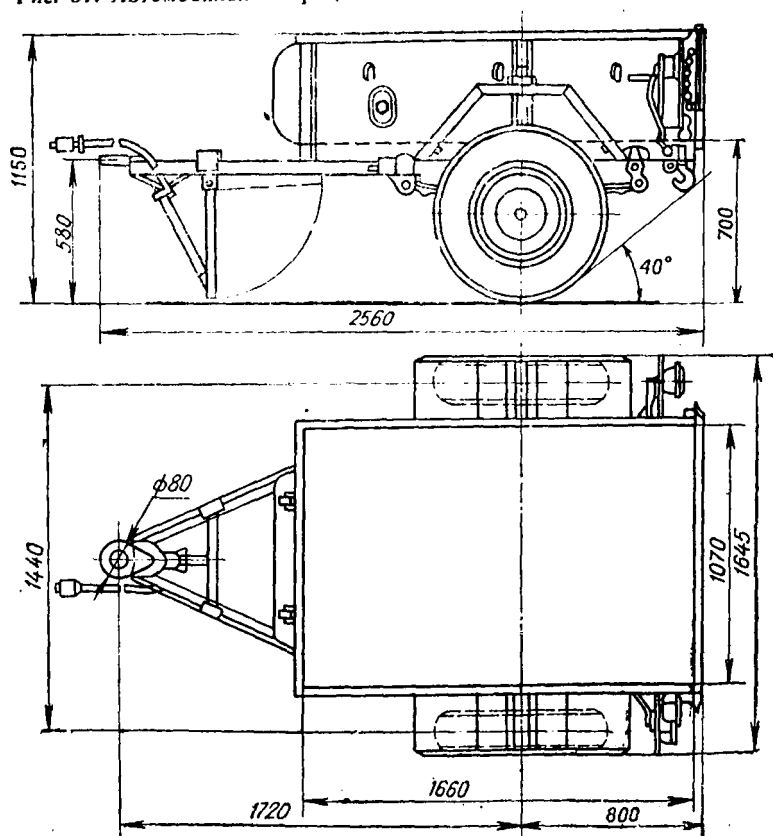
Схема автомобильного прицепа ГАЗ-704
